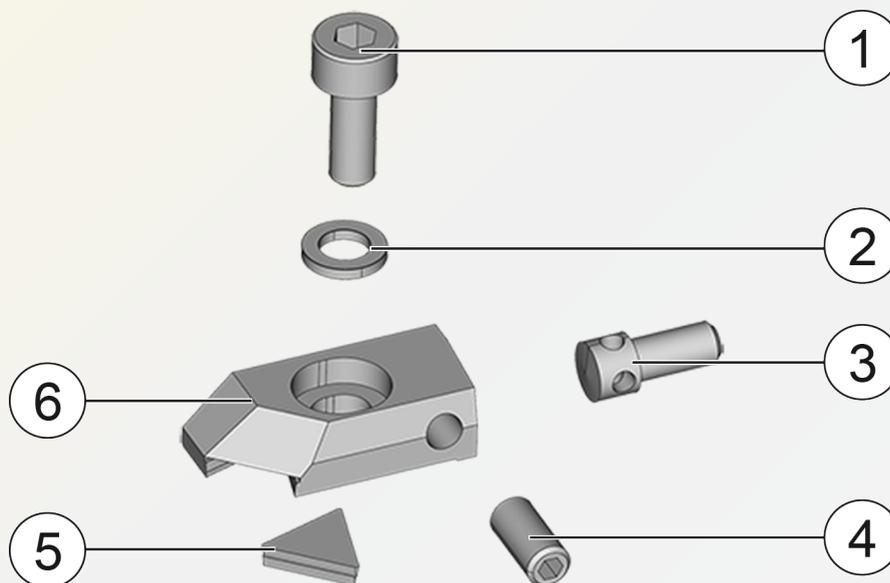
vue éclatée des outils avec l'élément de serrage réglable GP100
